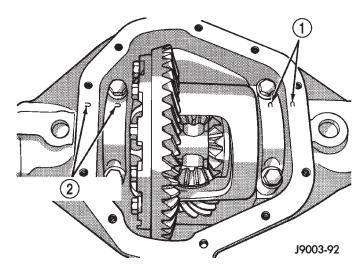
REFERENCIA DE TAPA DE COJINETE
